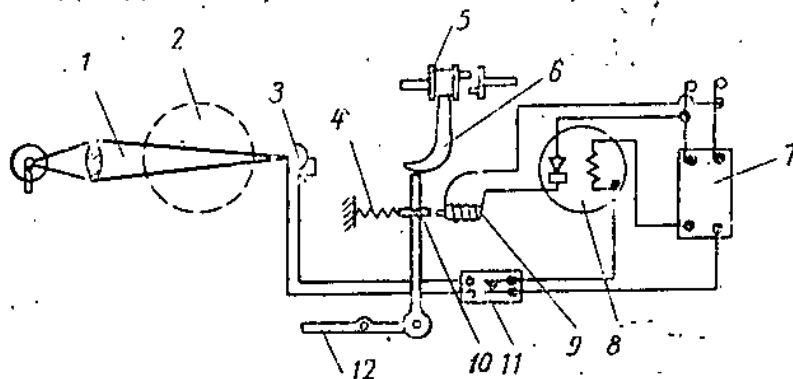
Схема блокировки пресса с кулачковой муфтой при помощи фотоэлемента
